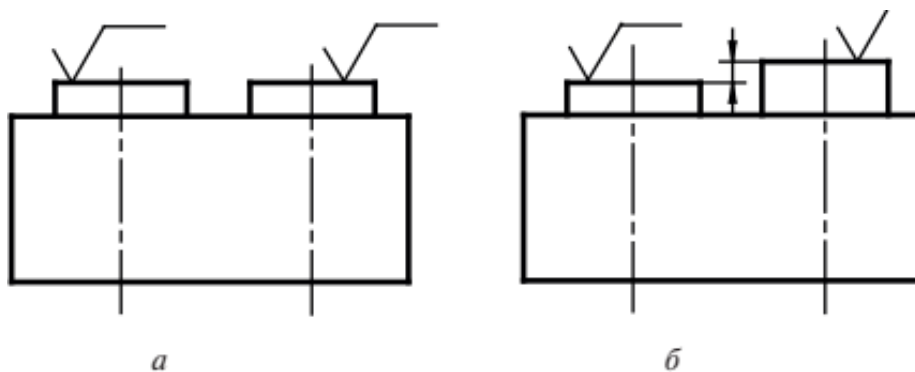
Конструкція корпусних деталей з бобишками:
